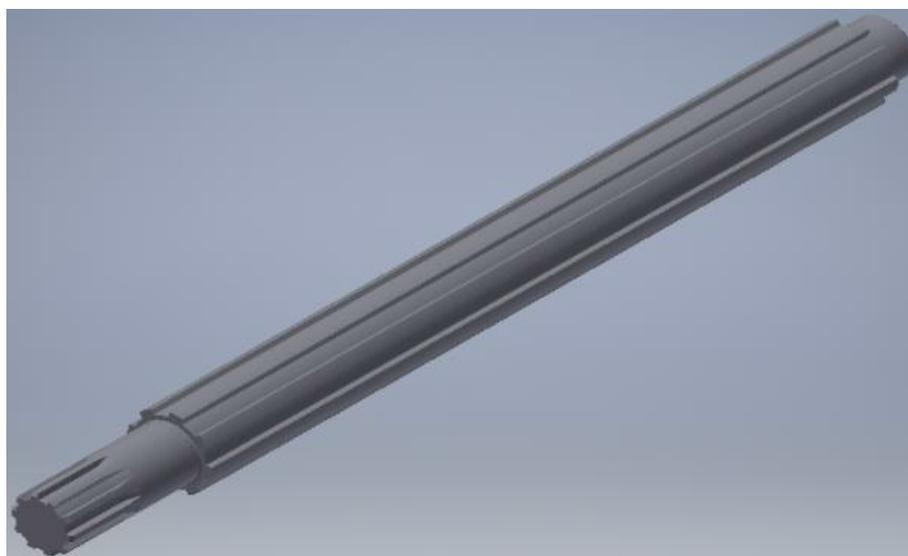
3D-модель вала коробки передач токарного станка
